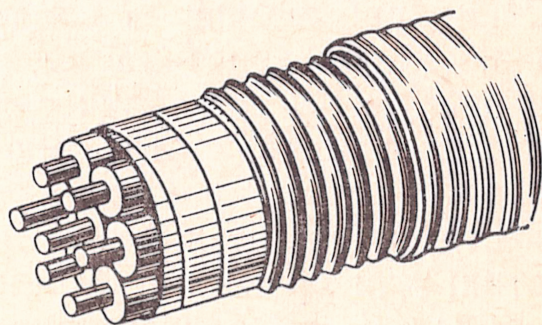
Внешний вид кабеля в сварной гофрированной оболочке.
